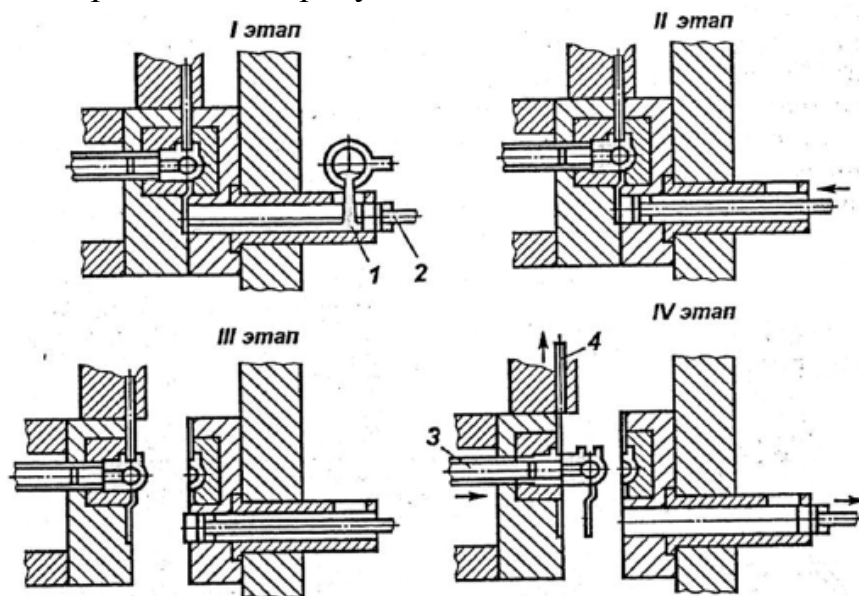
Схема процесса изготовления заготовки литьем под давлением: 1 – прессовальная камера; 2 – поршень; 3 – выталкиватель; 4 – стержень
